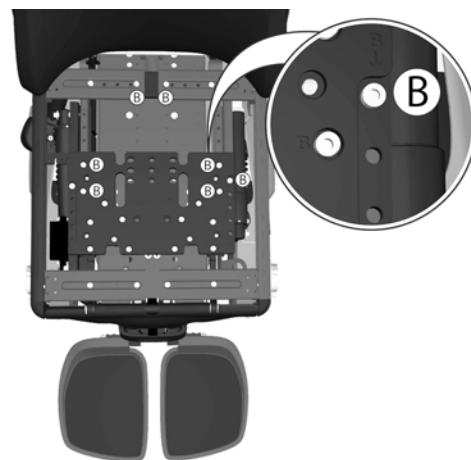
Die Position des hinteren Abschnitts des Sitzrahmens (Rückenlehnenposition) wird mit sieben Schrauben gehalten, die hier mit dem Buchstaben B markiert sind.
